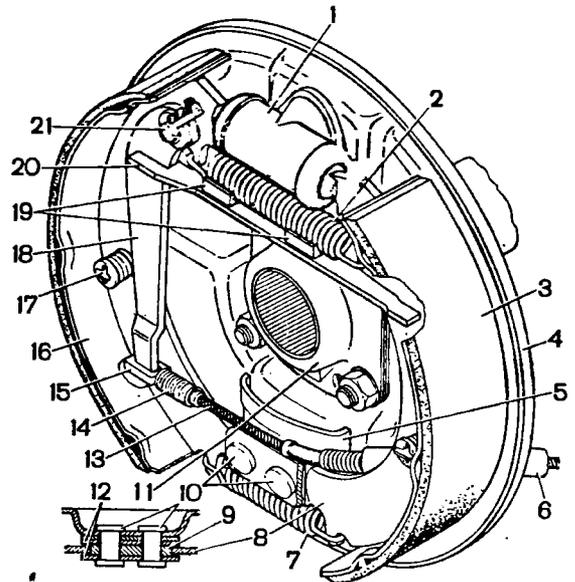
Тормозной механизм заднего колеса: 1 - колесный цилиндр; 2 - верхняя стяжная пружина колодок; 3 - накладка колодки; 4 - щит тормоза; 5 - внутренняя пластина; 6 - оболочка заднего троса; 7 - нижняя стяжная пружина колодок; 8 - передняя тормозная колодка; 9 - опорная пластина колодок; 10 - заклепки; 11 - маслоотражатель; 12 - направляющие пластины колодок; 13 - задний трос стояночного тормоза; 14 - пружина заднего троса; 15 - наконечник заднего троса; 16 - задняя тормозная колодка; 17 - опорная стойка колодки; 18 - рычаг ручного привода колодок; 19 - резиновые подушки; 20 - распорная планка колодок; 21 - палец рычага ручного привода колодок
